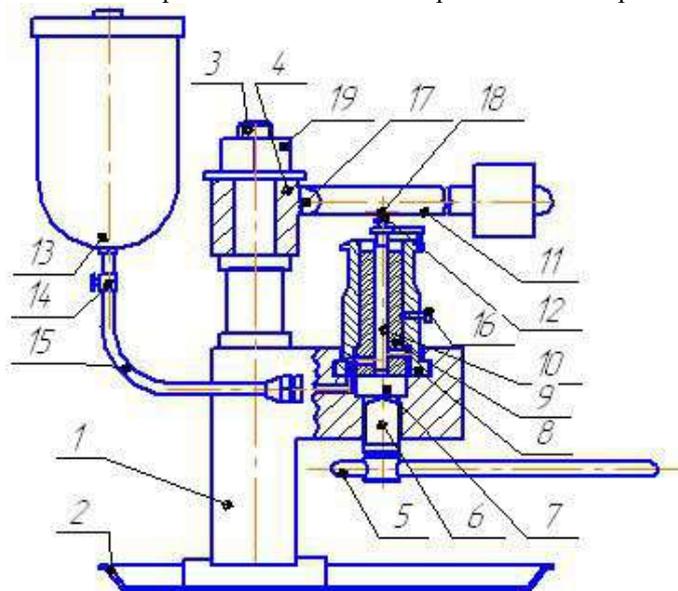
Устройство для статической опрессовки плунжерных пар: 1 – основание стойки; 2 – поддон; 3 – стойка; 4 – втулка 5 – вороток; 6 – винт; 7 – подпятник; 8 – корпус установочного механизма плунжерной пары; 9 – втулка плунжера; 10 – плунжер; 11 – рычаг с грузом; 12 – ролик; 13 – емкость для топлива; 14 – кран топливопровода; 15 – топливопровод; 16 – винт стопорный; 17 – ось рычага; 18 – ось ролика; 19 – гайка с шайбой.
